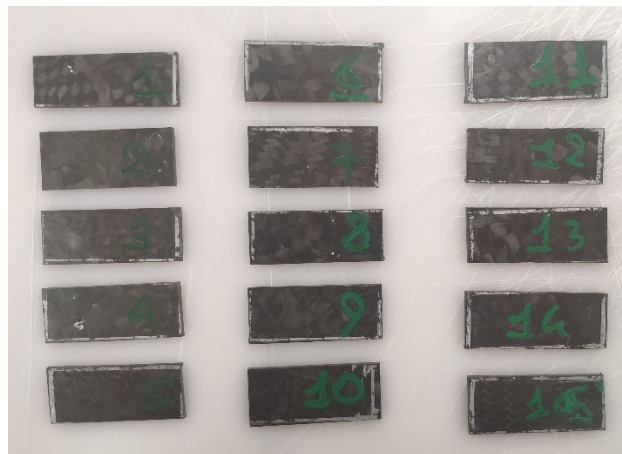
Provini ricavati dalle piastre 350x350mm
